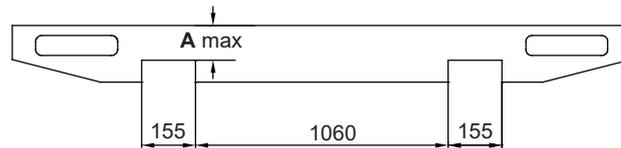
ZL-45-90, ZL-75-90, ZL-45-110, ZL-75-110
